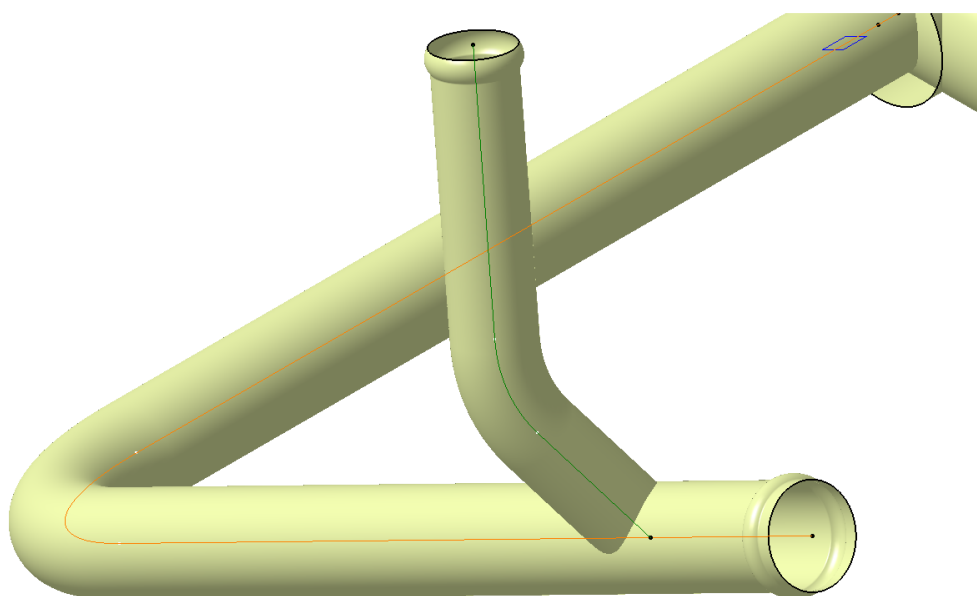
Образующая трубы отводящей радиатора отопителя
